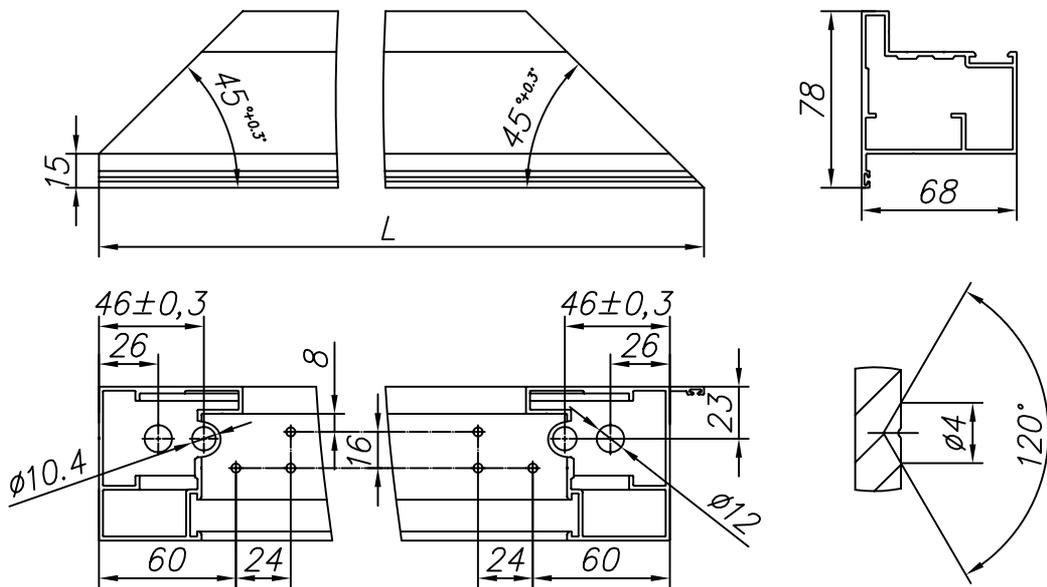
Изготовление стойки без паза для замка из профиля FLGU.400.0108 (калитка с перекладиной, открывание наружу, влево)
